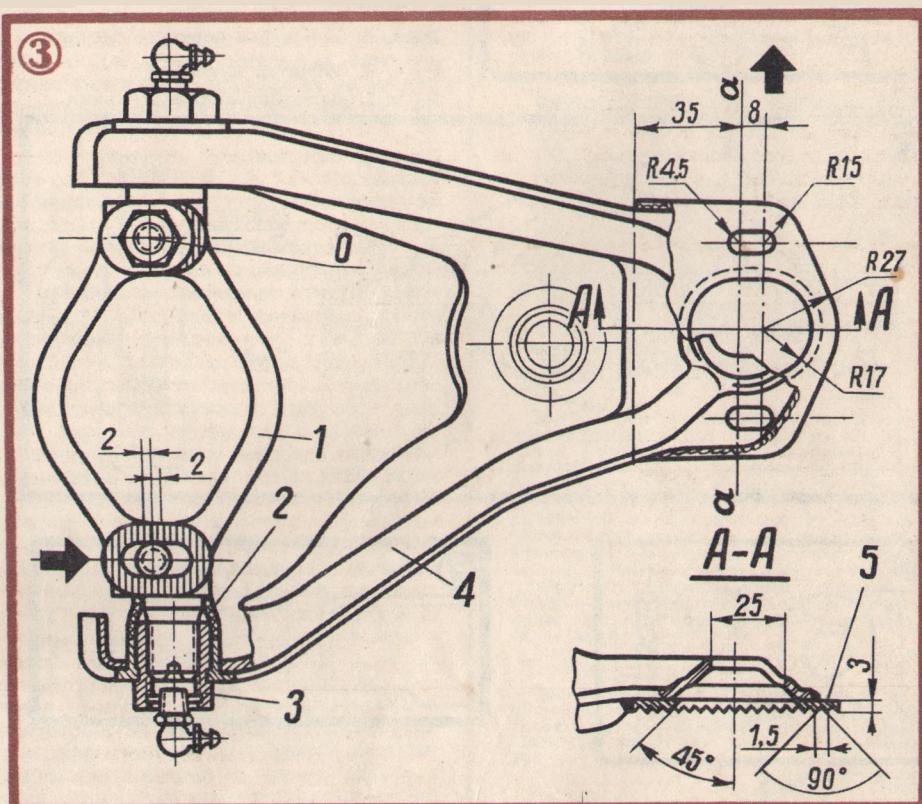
Измененный верхний рычаг: 1 — ось; 2 — резиновая втулка; 3 — резьбовая втулка; 4 — собственно рычаг; 5 — зубчатая пластина рычага.
